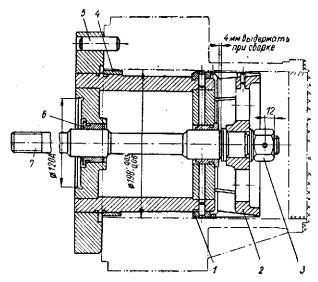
Цанговая оправка с пневмоприводом для обработки крупных втулок
